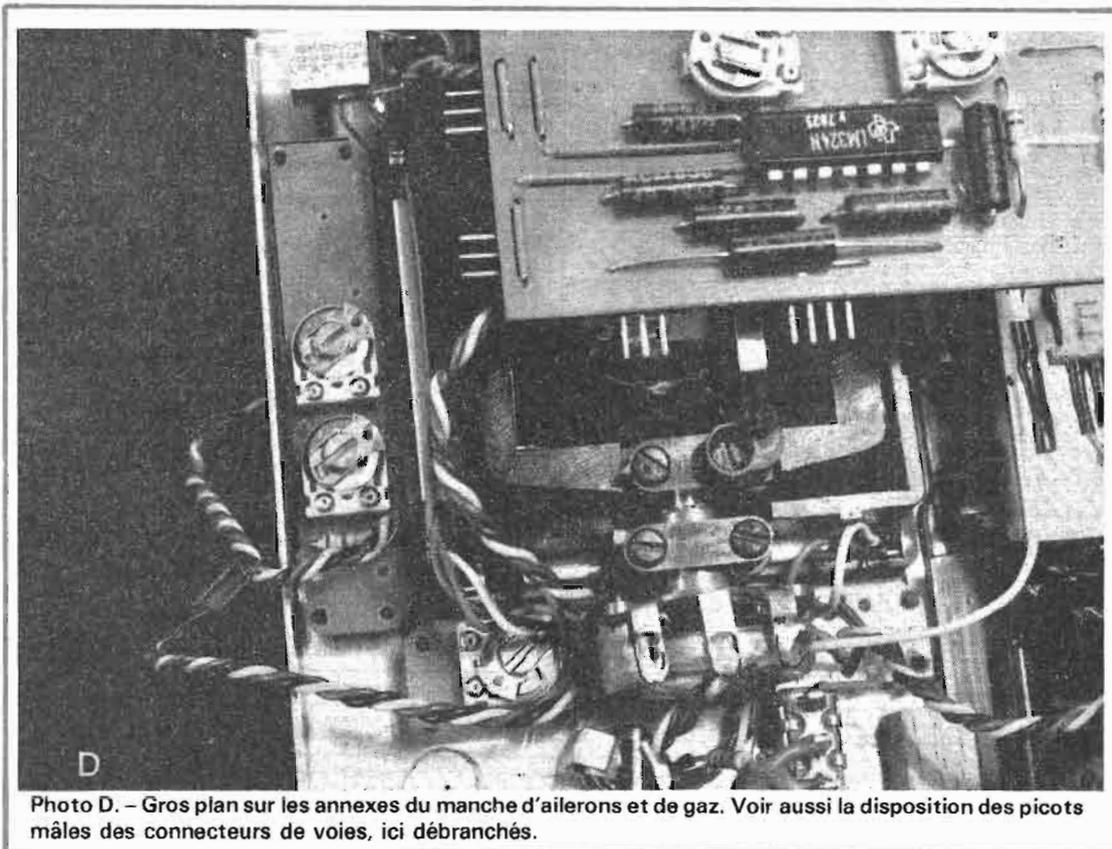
Photo D. - Gros plan sur les annexes du manche d'ailerons et de gaz. Voir aussi la disposition des picots mâles des connecteurs de voies, ici débranchés.
